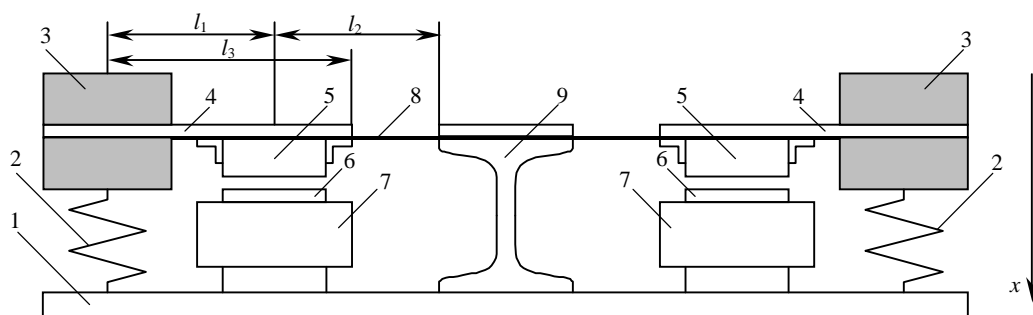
Электромагнитный вибратор с двумя симметрично расположенными реактивными массами: 1 – основание; 2 – пружина; 3 – реактивная масса; 4 – рычаг; 5 – якорь; 6 – сердечник; 7 – обмотка; 8 – упругая пластина; 9 – стойка
